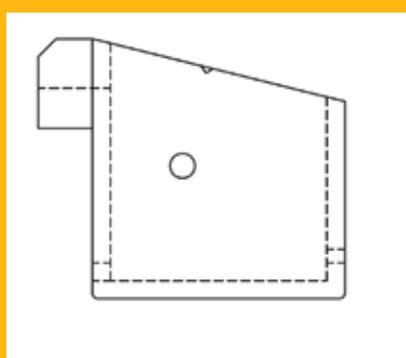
типичная напорная коробка поворотной литейной машины
